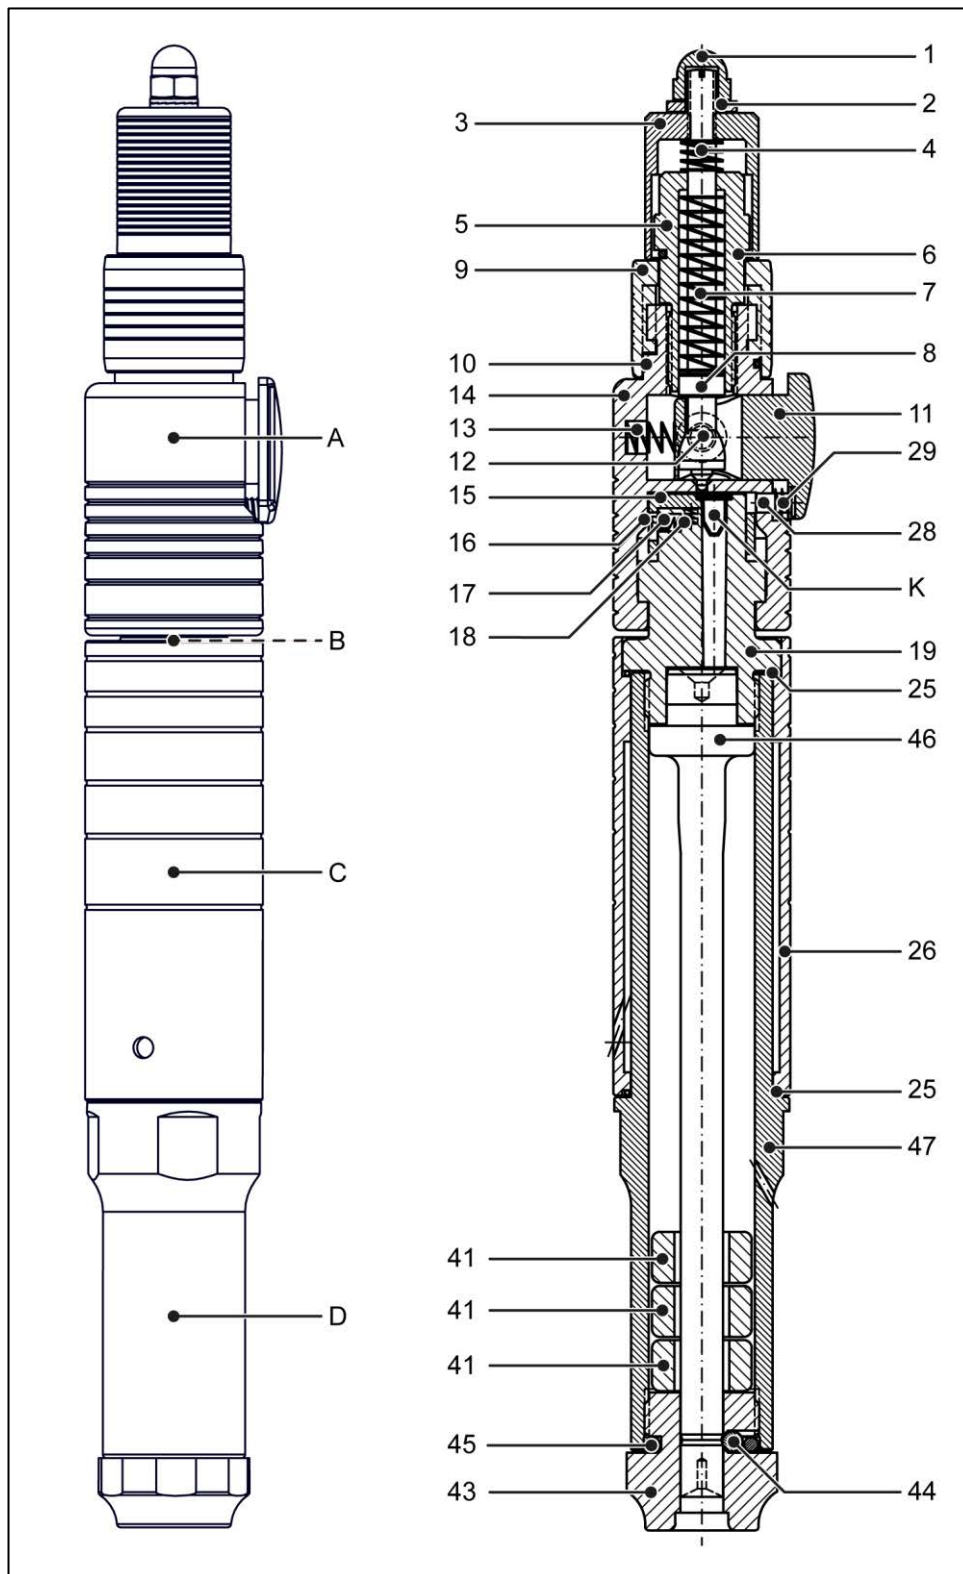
Baugruppen/Bauelemente Typ KL
